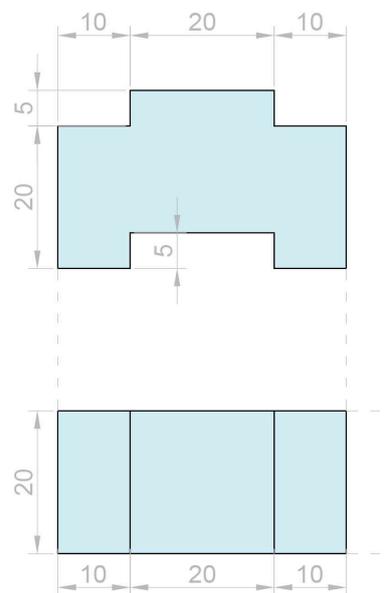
Dimensiones módulo de plástico reciclado, alzado frontal y planta. Elaboración propia.
